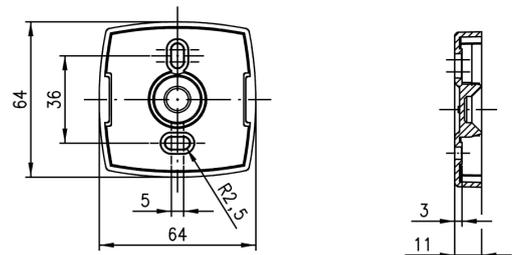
Draufsicht und Querschnitt von der Adapterplatte
